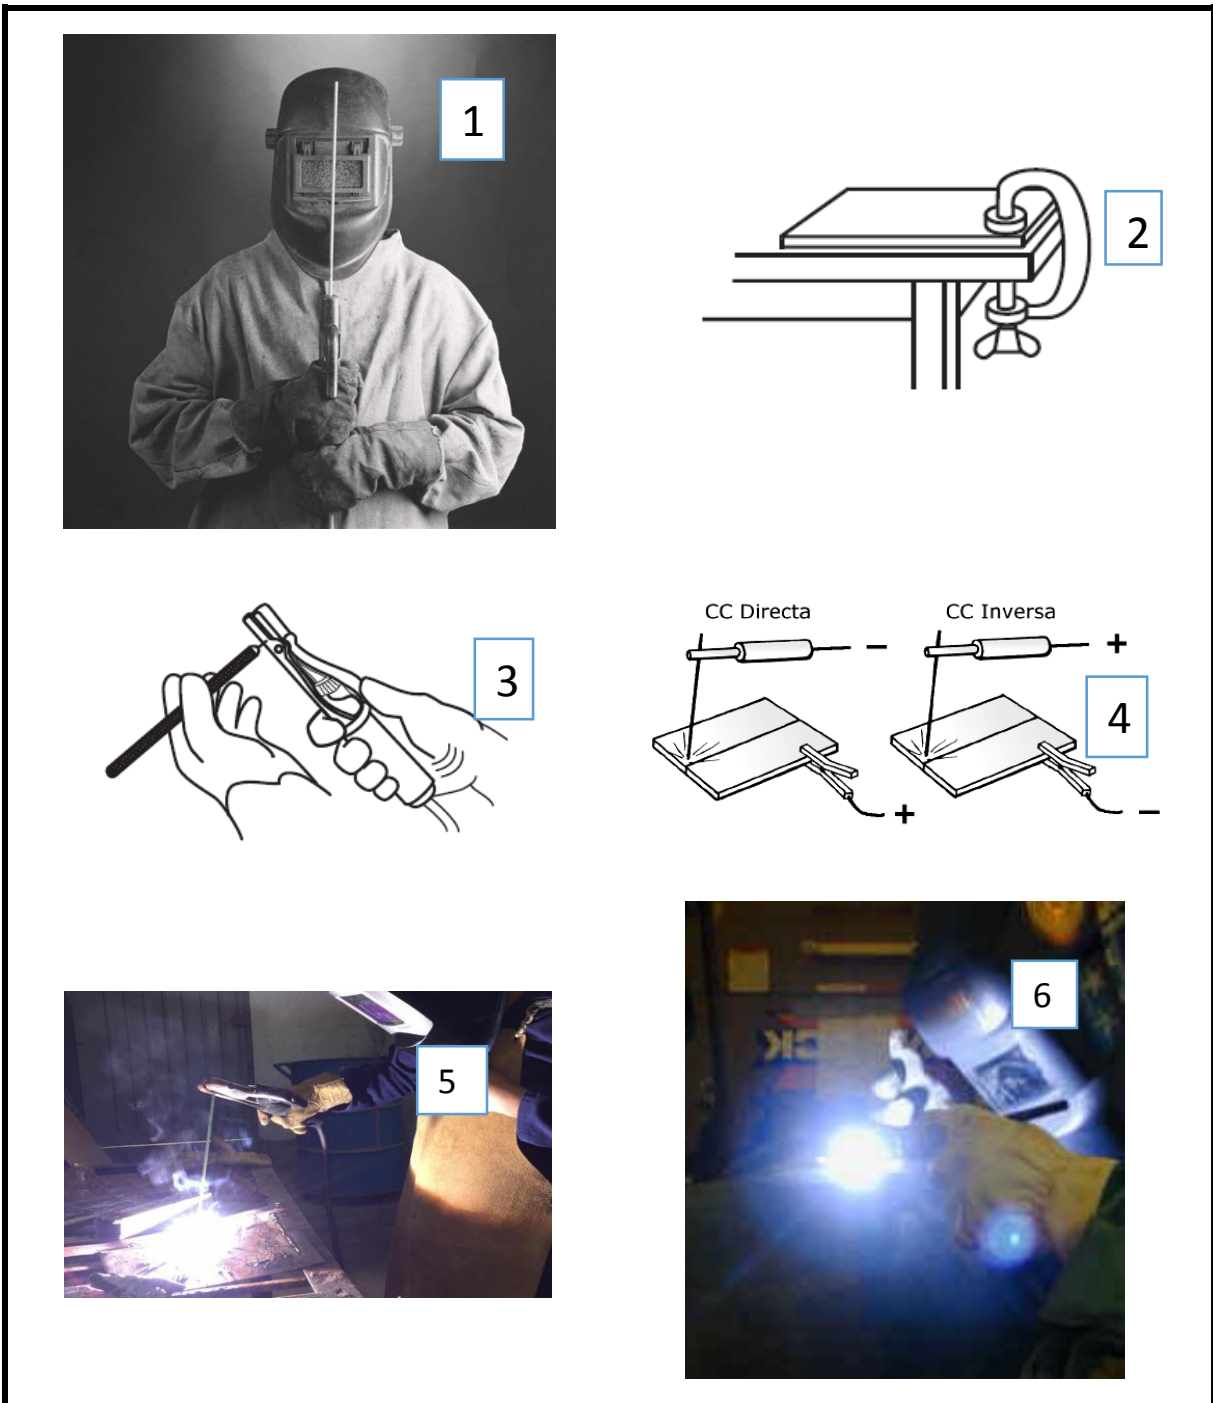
Material utilizado para el proceso de soldadura.
